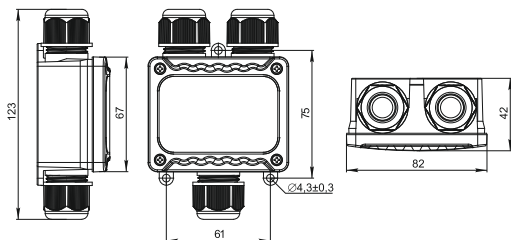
Габаритные размеры коробки WTP-401 / Figure 1 – Overall dimensions of the WTP-401 box
